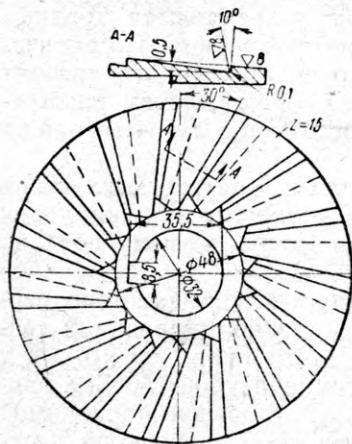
Фреза для снятия нагара и полуды со шлицев коллекторных пластин
